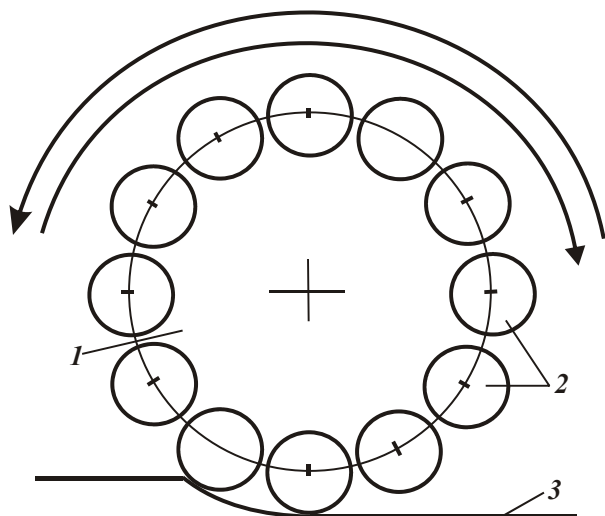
Схема шлифования плоскими кругами прямого профиля: 1 - вращающийся несущий диск; 2 - плоские прямые круги; 3 - обрабатываемая поверхность.
